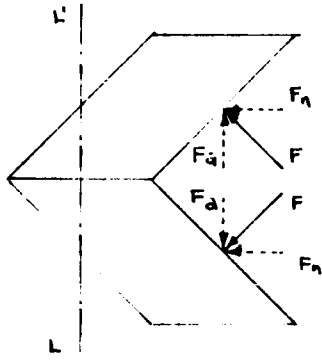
Montaje de dos engranes de dientes helicoidales para anular la carga axial
